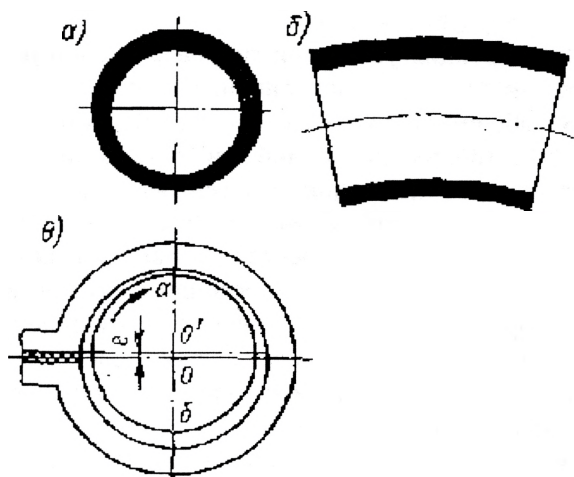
Коробление валика с неравномерным по глубине закаленным слоем, вызываемое неправильной центровкой изделия:  $O$  – выточки на торцах валика для установки его в центрах станка;  $O'$  – геометрическая ось валика
